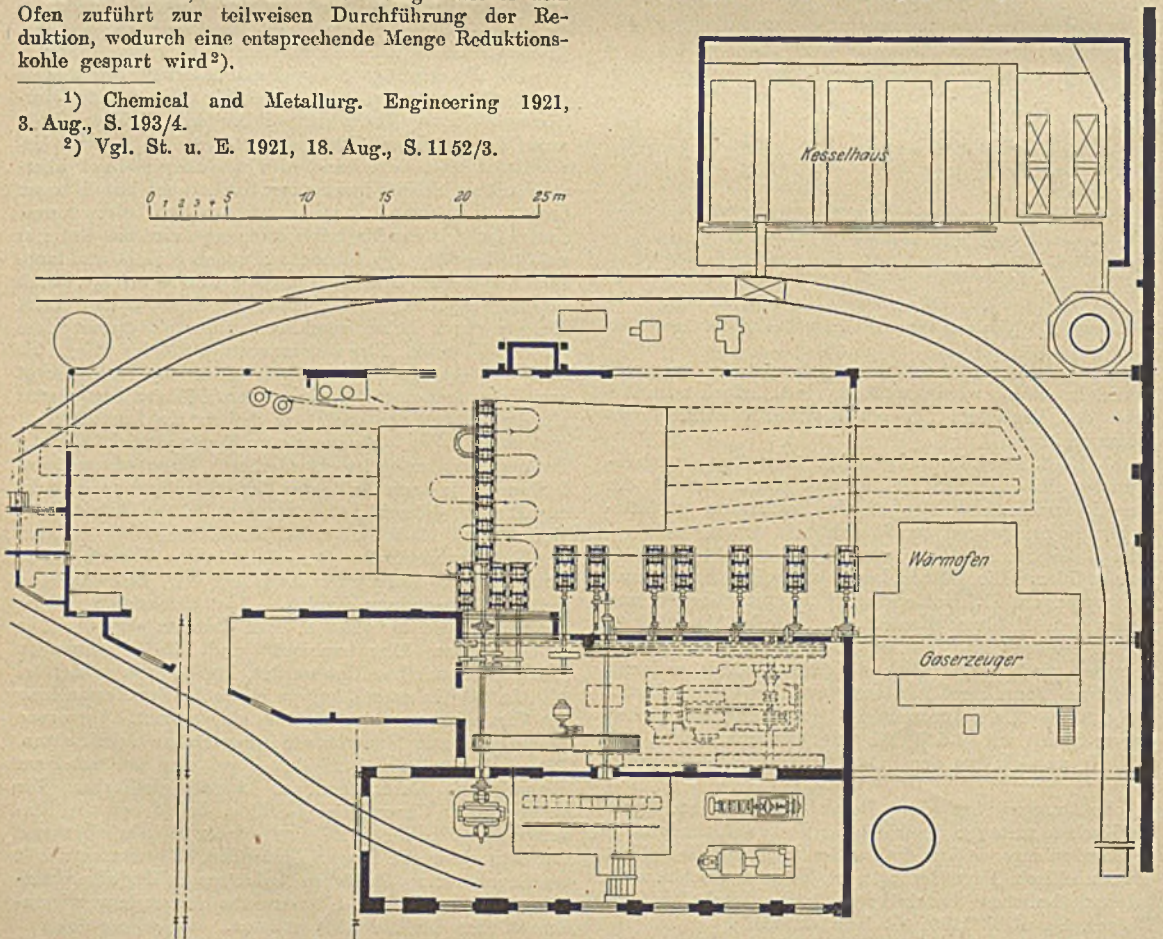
Umbau des Antriebes im Drahtwalzwerk der Whitecross Steel Co.
